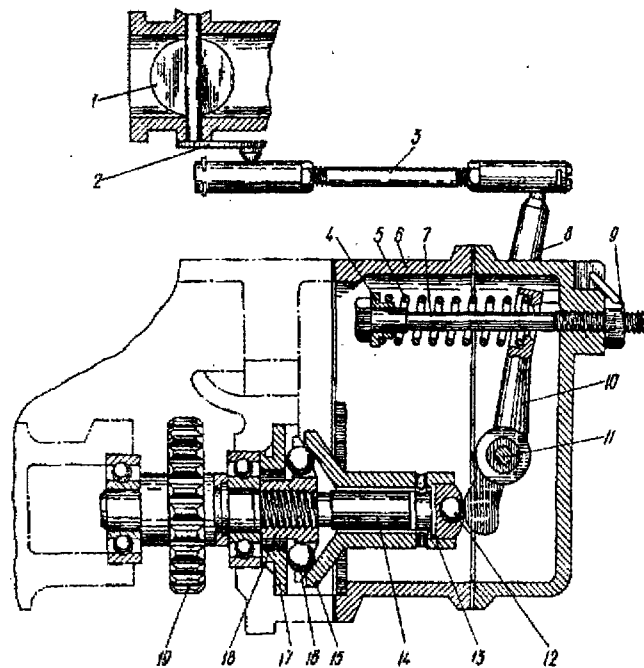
Регулятор пускового двигателя: 1 – дроссельная заслонка; 2 – рычажок с поводком; 3 – тяга; 4 – втулка; 5 – пружина; 6 – корпус; 7 – регулировочный винт; 8 – наружный рычаг; 9 – контртяга; 10 – двуплечий рычаг; 11 – ось рычага; 12 и 16 – шарики; 13 – шайба; 14 – валик; 15, 17 и 18 – подвижный, опорный и ведущий диски; 19 – шестерня привода
